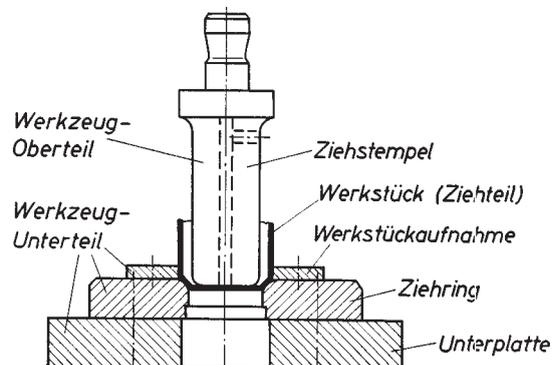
Umformwerkzeug ohne Führung (Ziehwerkzeug)
